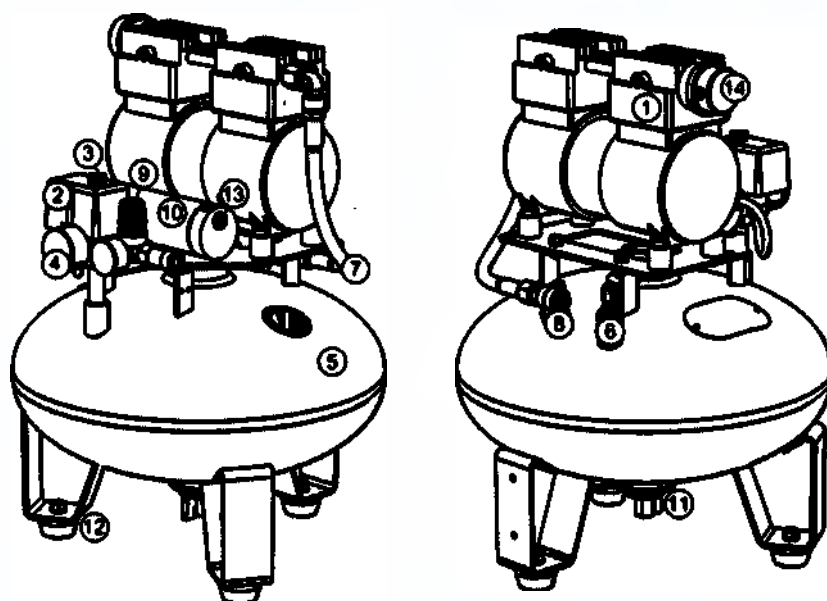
Общий вид компрессора KM-24.OLD10
